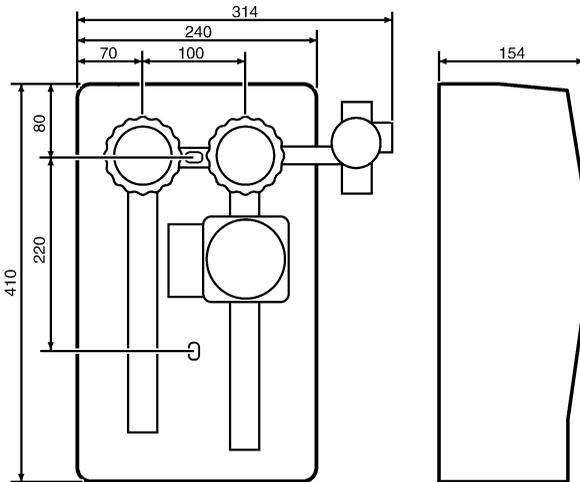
Dimensioni [mm] PrimoSol® 130-2/-3/-4
